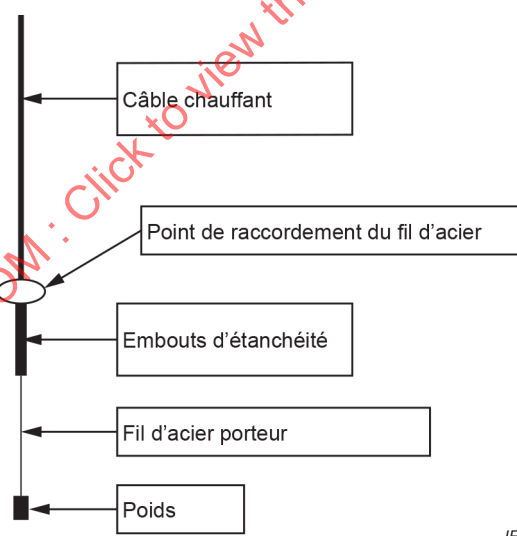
Installation d'essai typique de l'embout d'étanchéité
